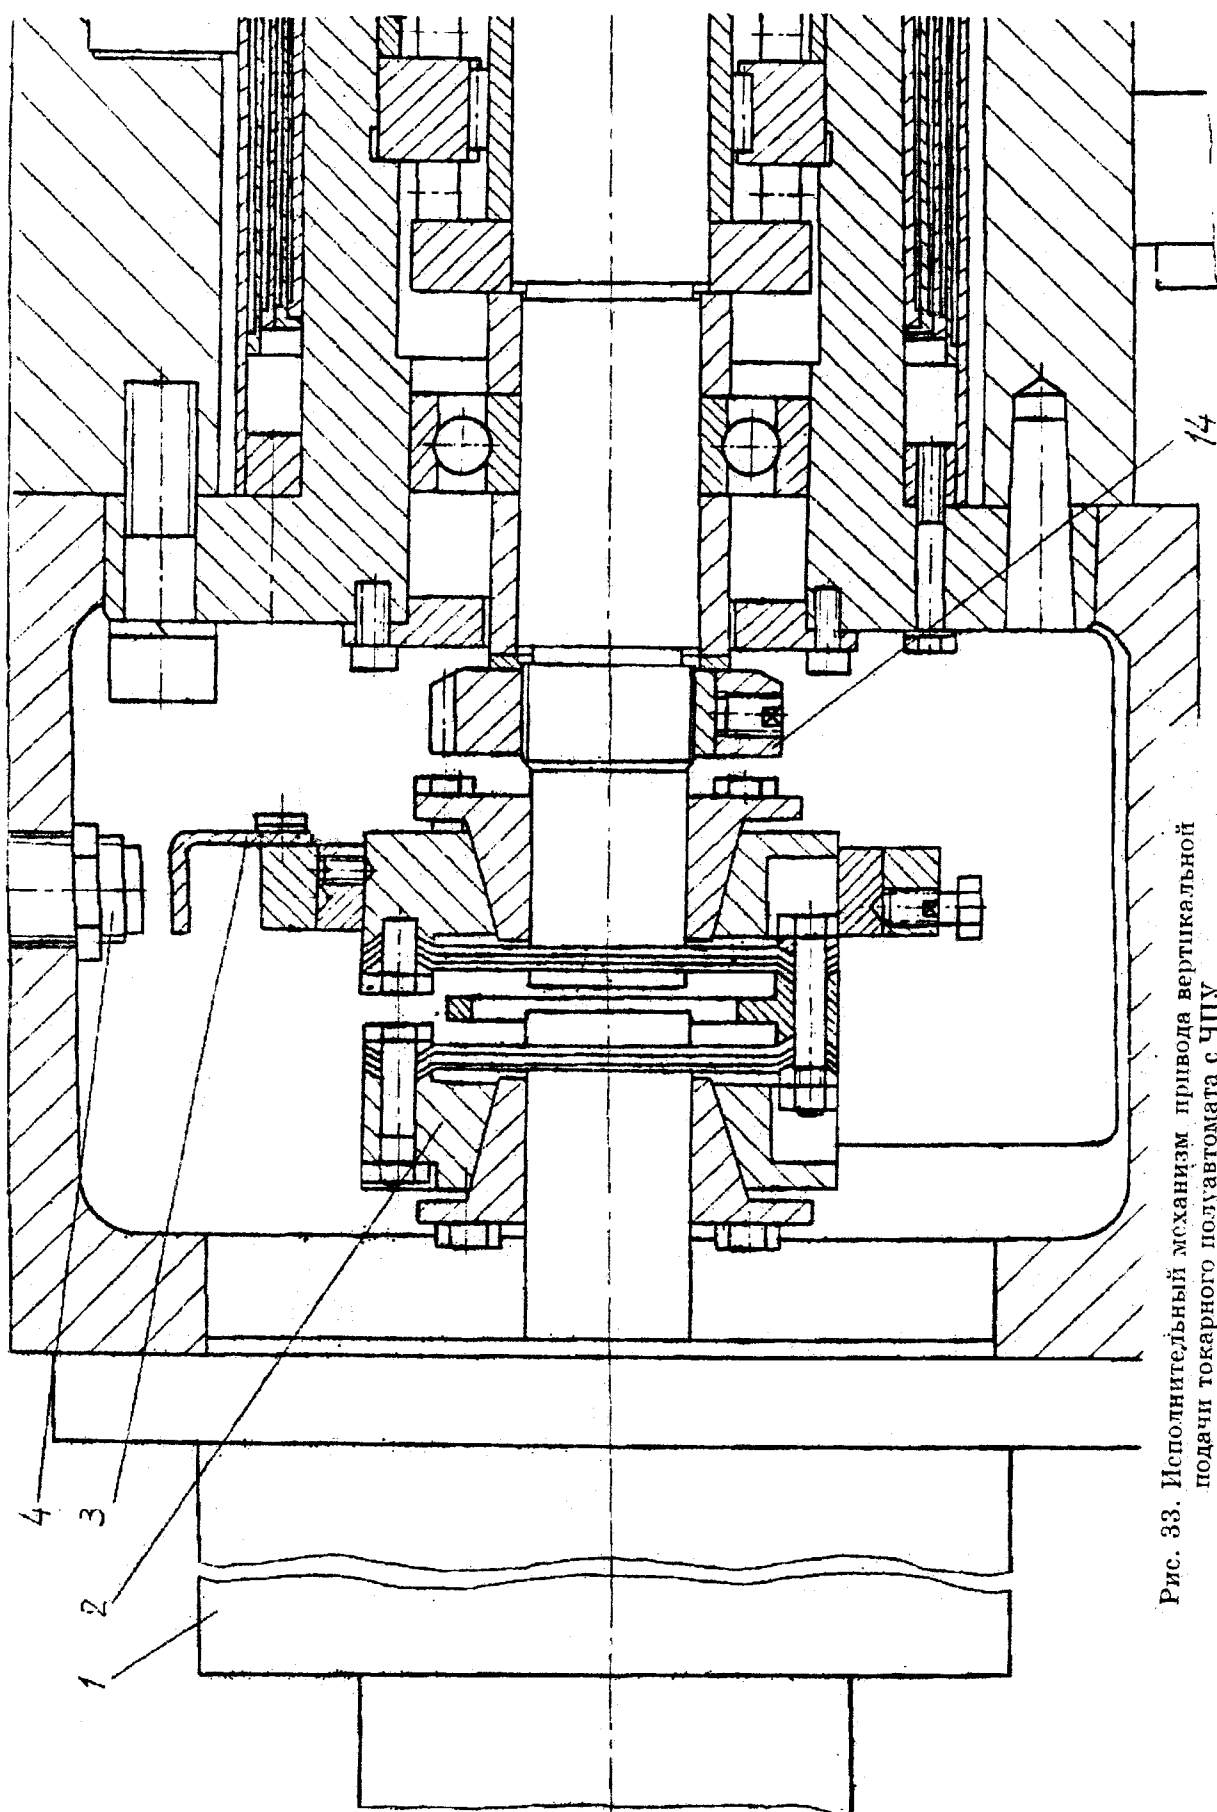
Исполнительный механизм привода вертикальной подачи токарного полуавтомата с ЧПУ
